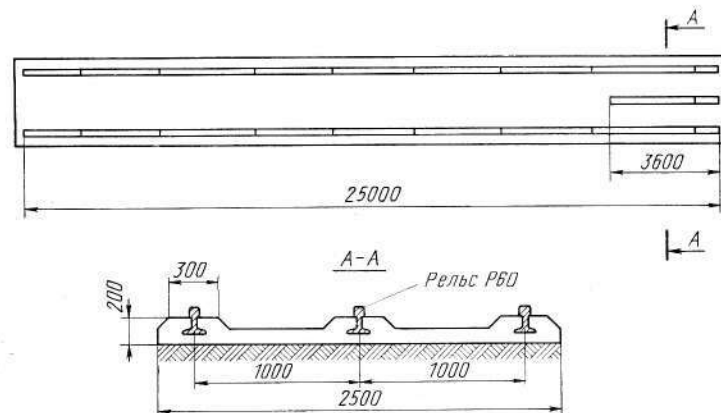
Стенд для укрупнительной сборки узлов прокатного оборудования
